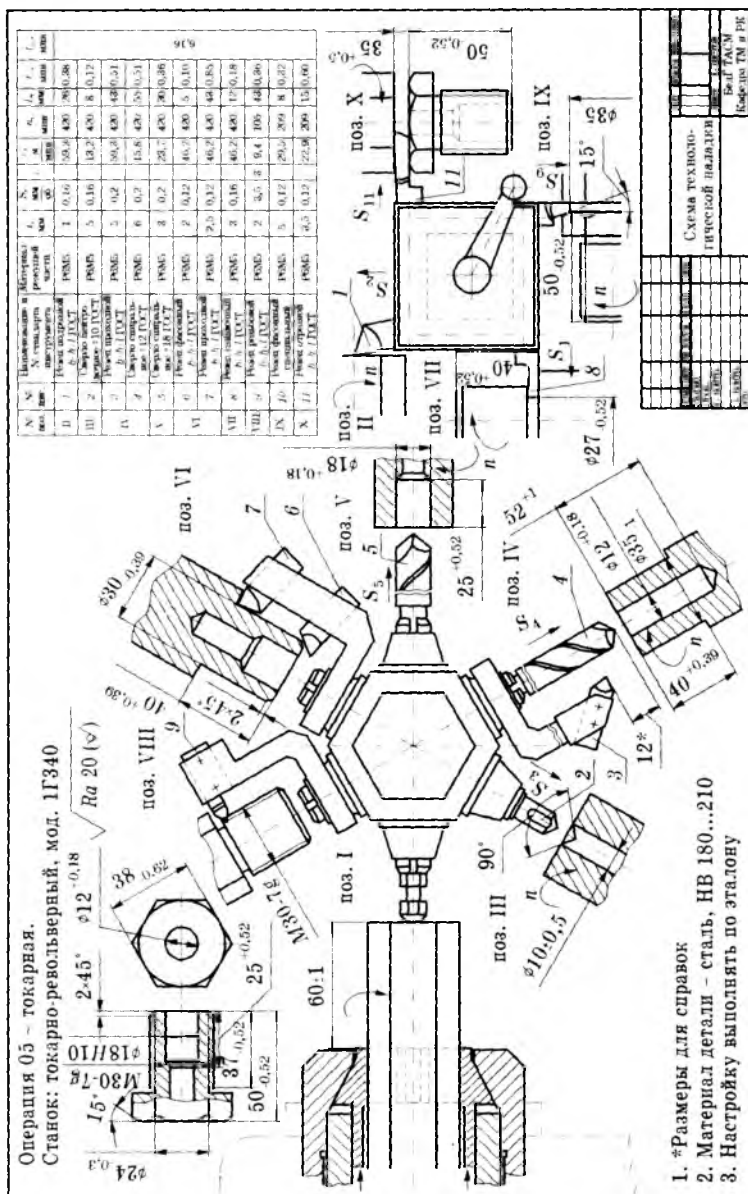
Схема технологической наладки токарно-револьверного станка
